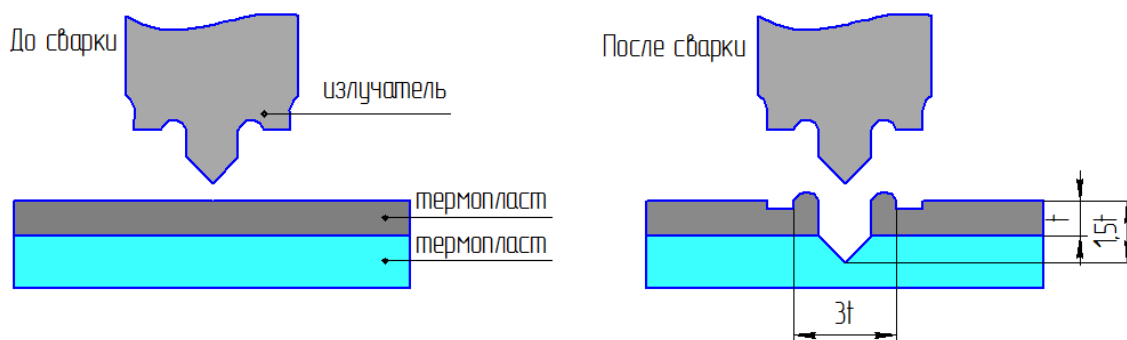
Схема ультразвуковой точечной сварки термопластичных полимеров
